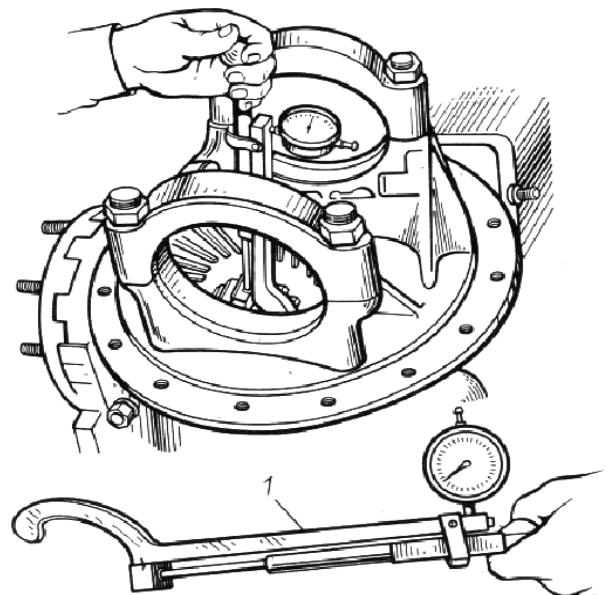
Проверка затяжки подшипников динамометрической рукояткой:
